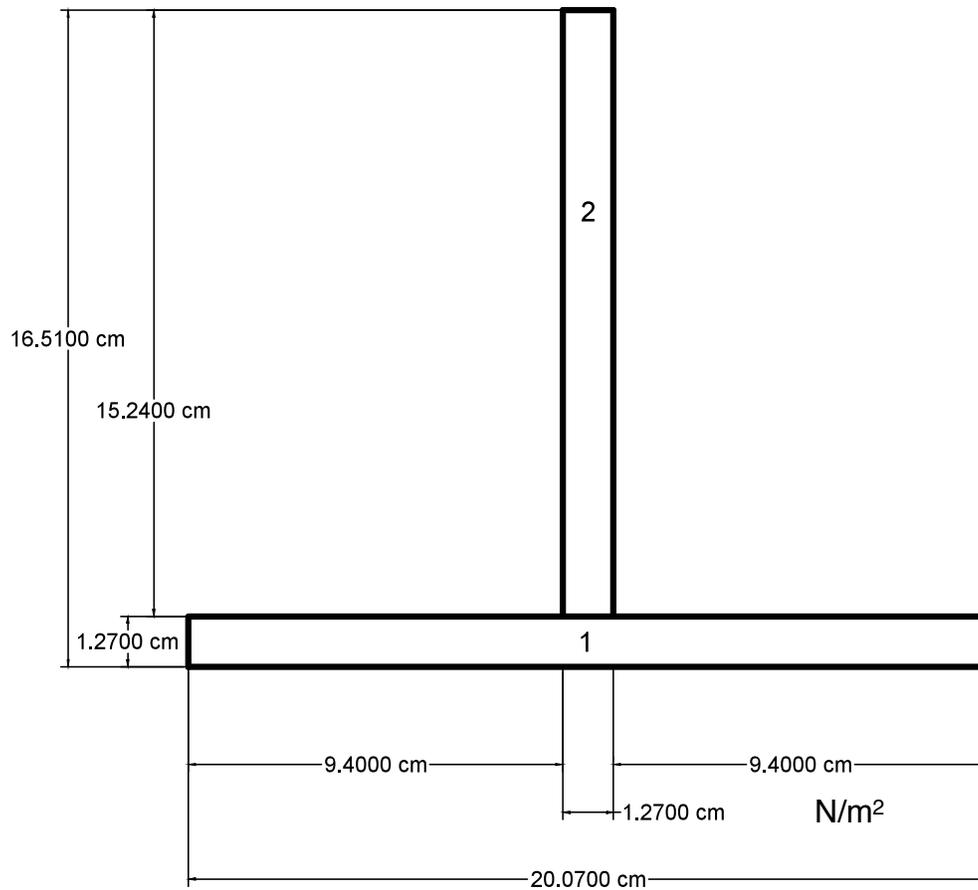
Vista lateral de elementos soldados a chasis
